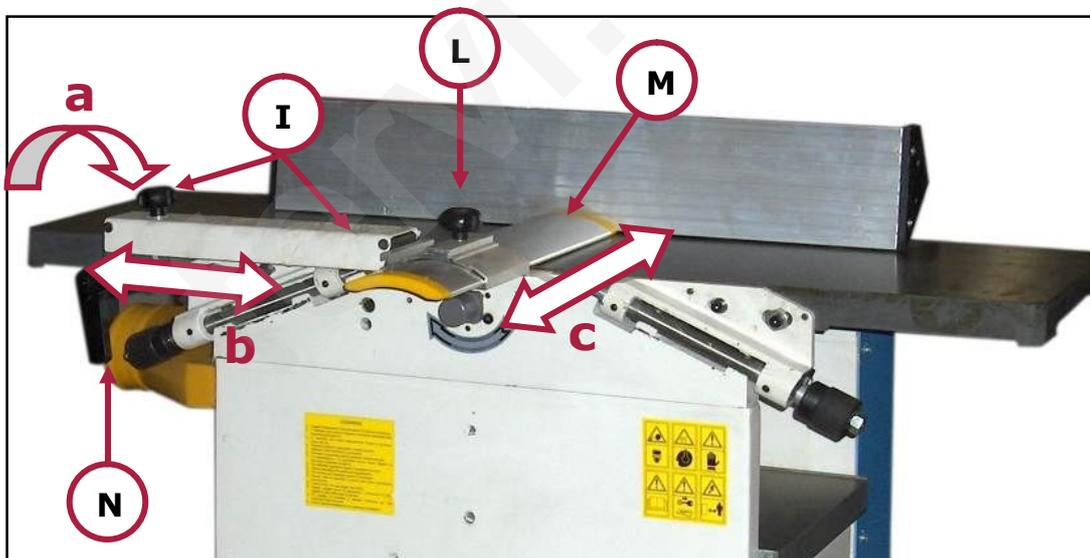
Regolazione del riparo anteriore dell'albero pialla.
